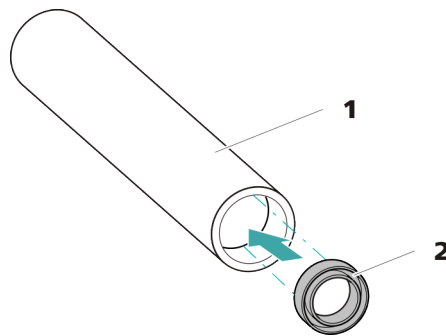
Kolbendichtung in Werkzeug einsetzen
